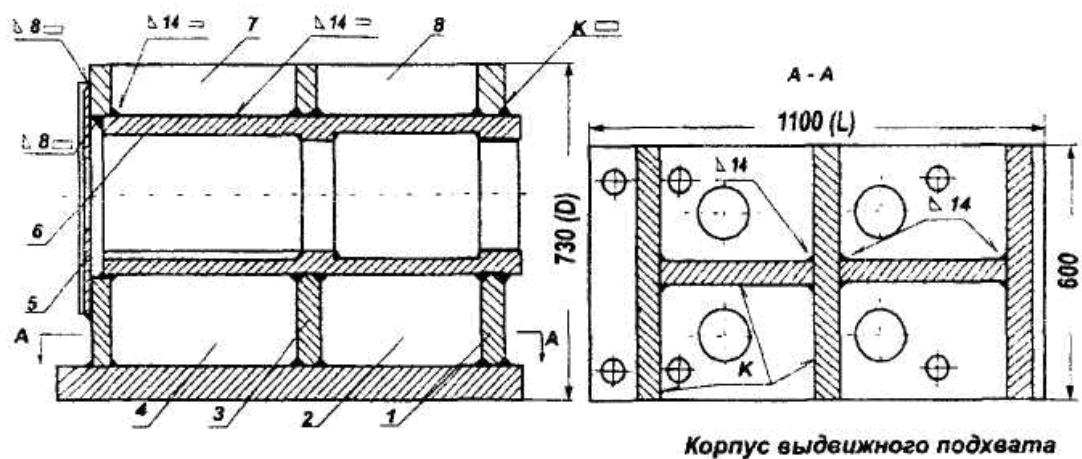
Эскизы корпуса выдвижного подхвата и его деталей для задания № 5
